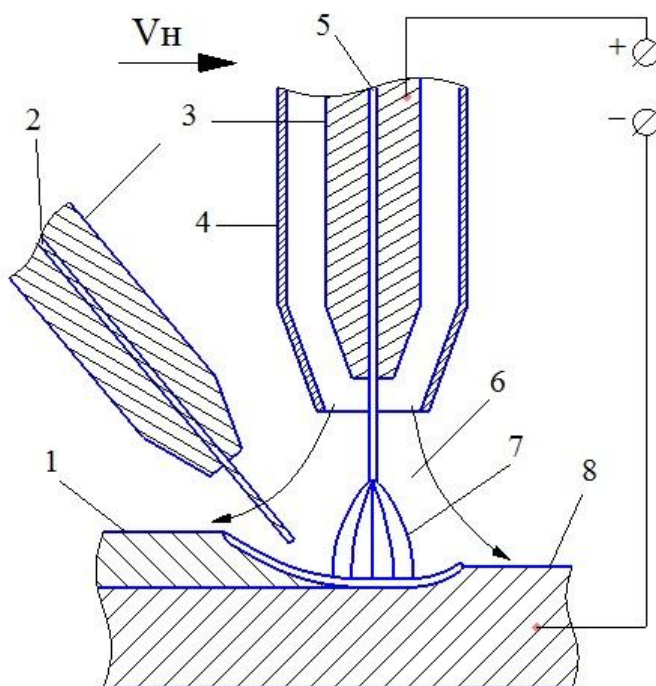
Схема процесса сварки (наплавки) в защитных газах с дополнительной холодной проволокой
